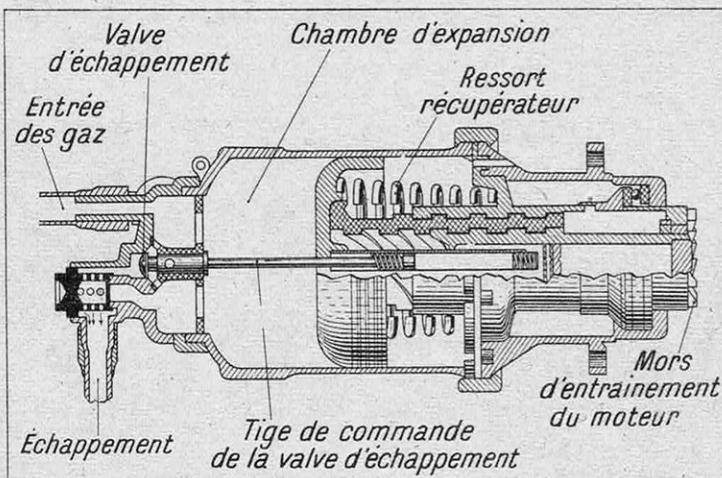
SCHÉMA DU DÉMARREUR A EXPLOSION
